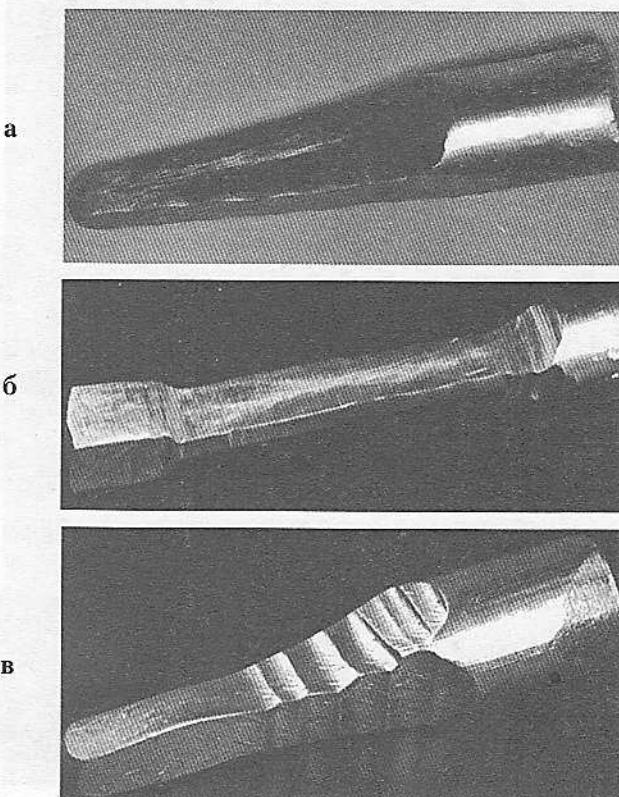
Заготовки под штамповку после протяжки на ковочном молоте
